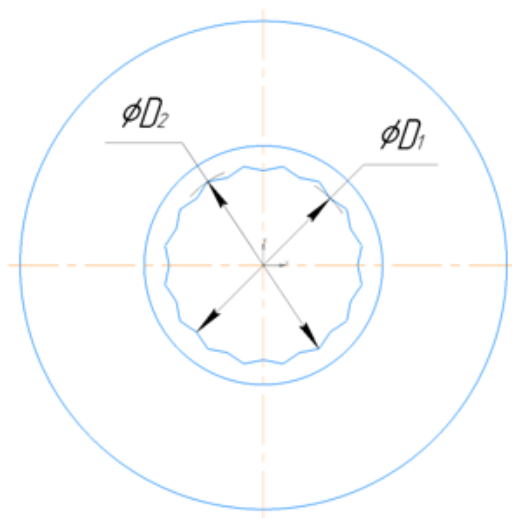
Матрица для вытяжки с локальным утонением стенки заготовки.
